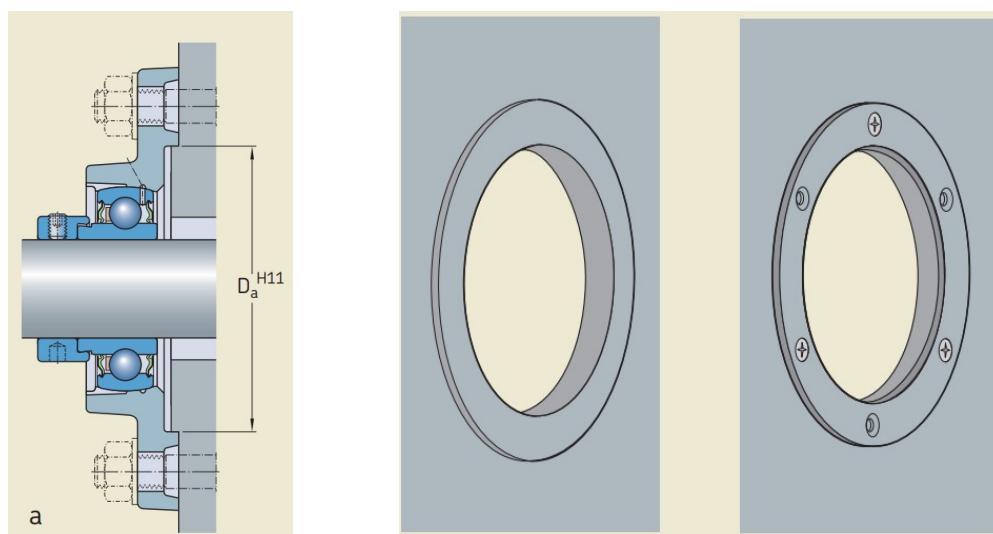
Rebaje para el ajuste del rodamiento.
